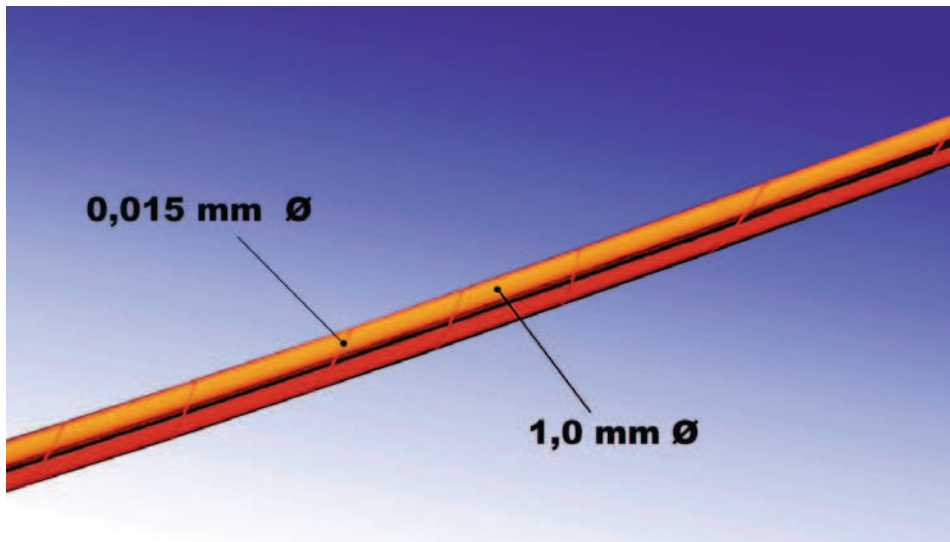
Dimensionen der verschiedenen Drahthalbzeuge
